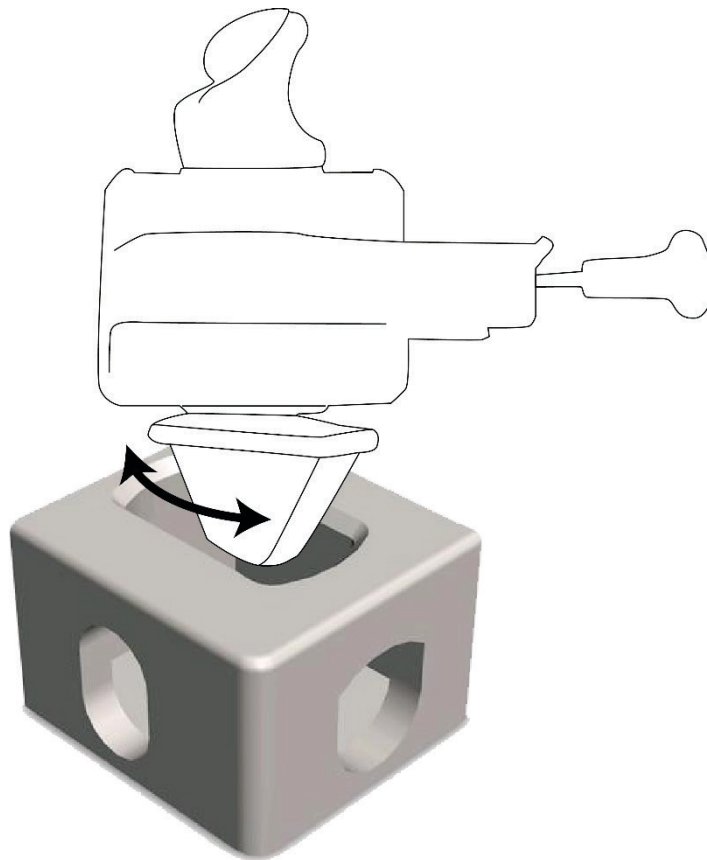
Prinzipskizze der Verriegelung eines Twist Locks in einem Corner Casting
